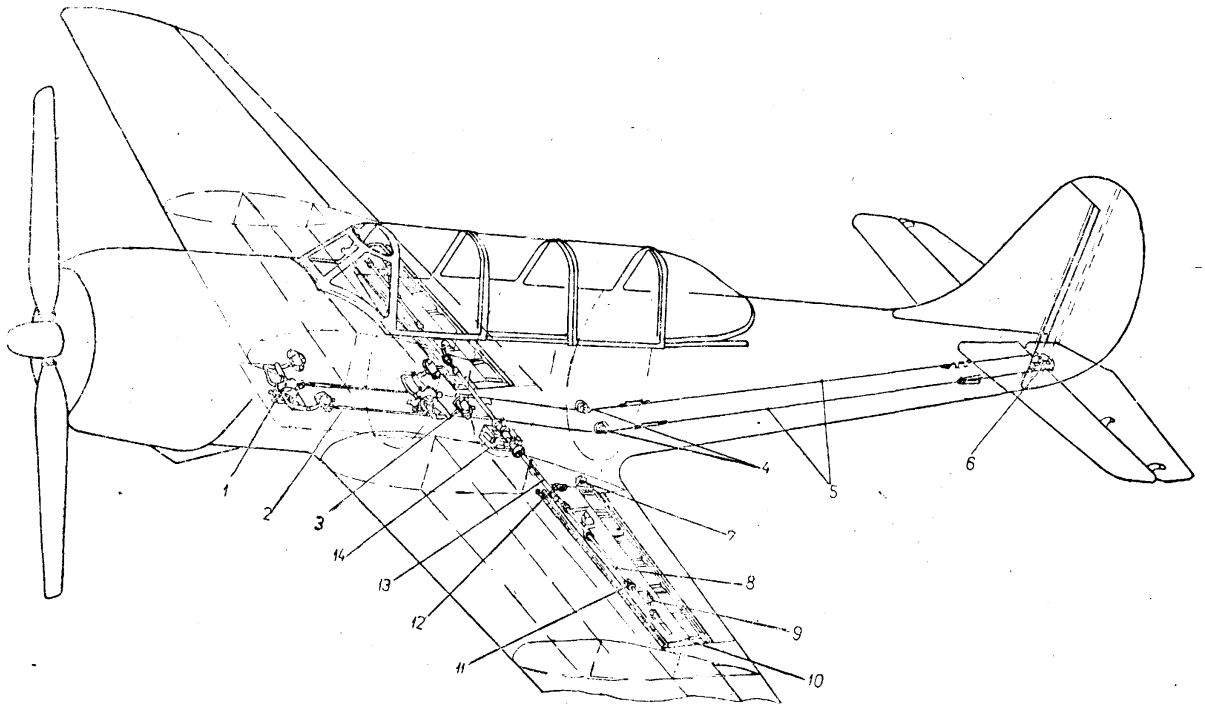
УПРАВЛЕНИЕ РУЛЕМ НАПРАВЛЕНИЯ И ПОСАДОЧНЫМИ ЩИТКАМИ
